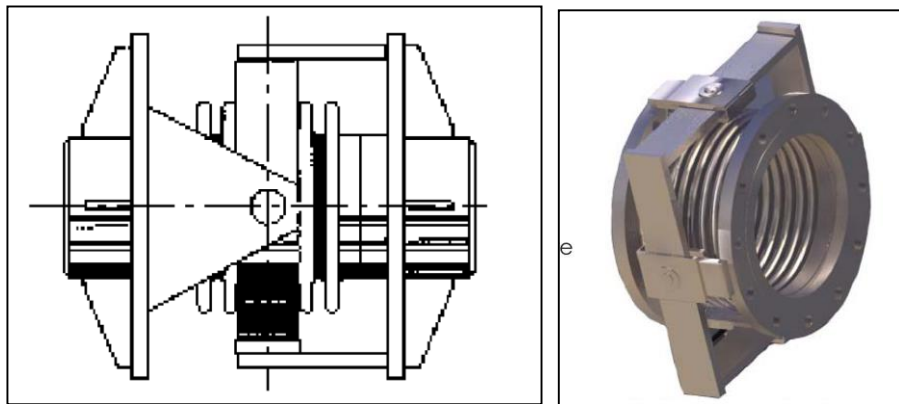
Junta de expansión cardánica ("gimbal expansion joint").
